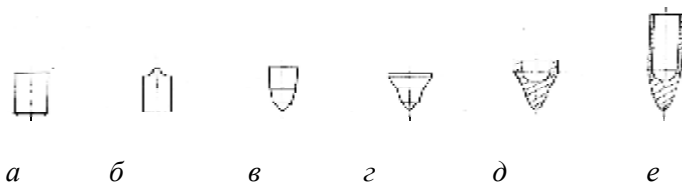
Эскизы поковок: *а* – поковка после осадки-калибровки исходной прутковой заготовки; *б* – поковка после формирования вершинного участка будущей головной части оболочки; *в* – поковка после формирования конического элемента, прилегающего к вершинному участку; *г* – поковка после формирования элементов, используемых для последующего формообразования основания головной части оболочки и ее хвостового участка; *д* – поковка после предварительного формообразования головной части оболочки и ее хвостового участка; *е* – поковка после второй вытяжки хвостовой части оболочки
